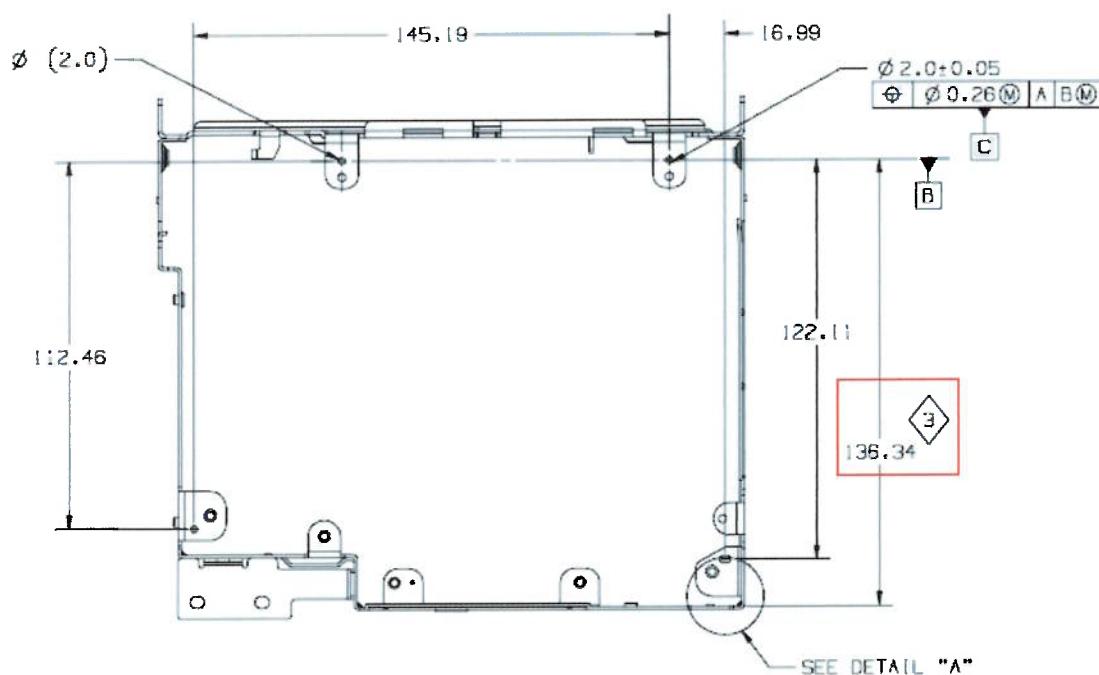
Detalhe da dimensão crítica no desenho do produto
